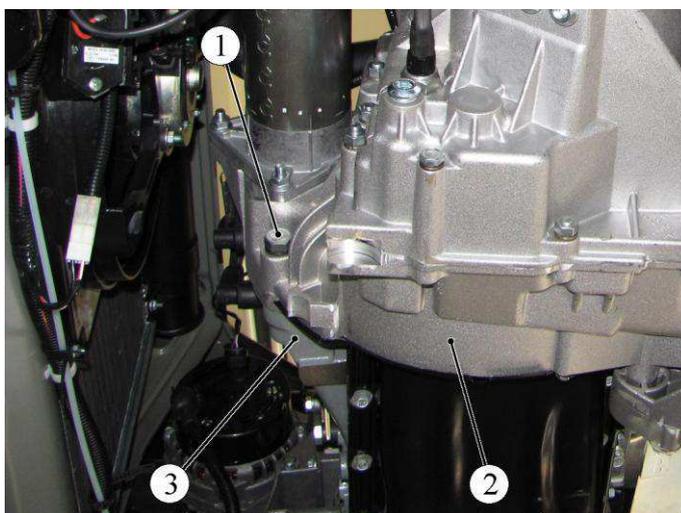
Отсоединение коробки передач от двигателя:
